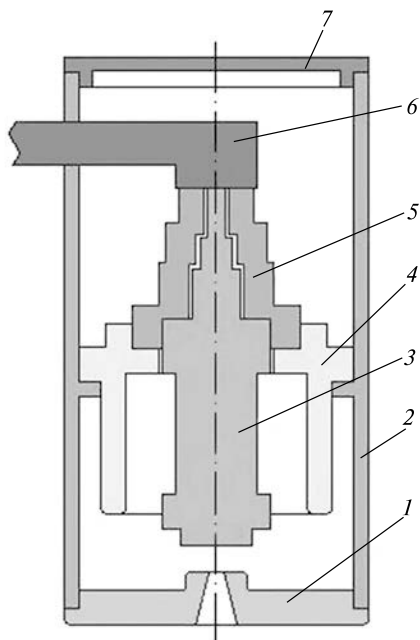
Загальна компоновка нової електронно-променевої зварювальної гармати [11]: 1 — анодний блок, 2 — корпус, 3 — з'ємний катодний вузол, 4 — високовольтний ізолятор, 5 — головний ізолятор катодного вузла, 6 — високовольтне введення, 7 — кришка
